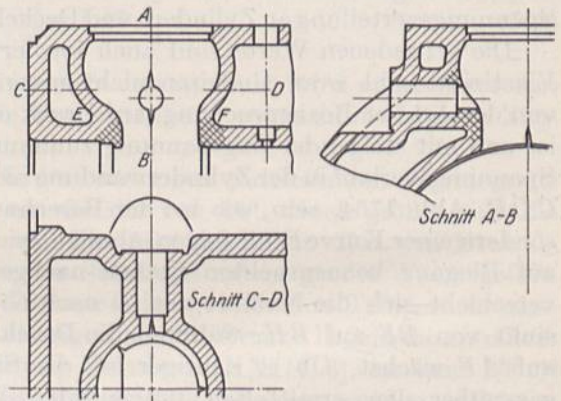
Zwiebelrisse an Großgasmaschinenzylindern.
